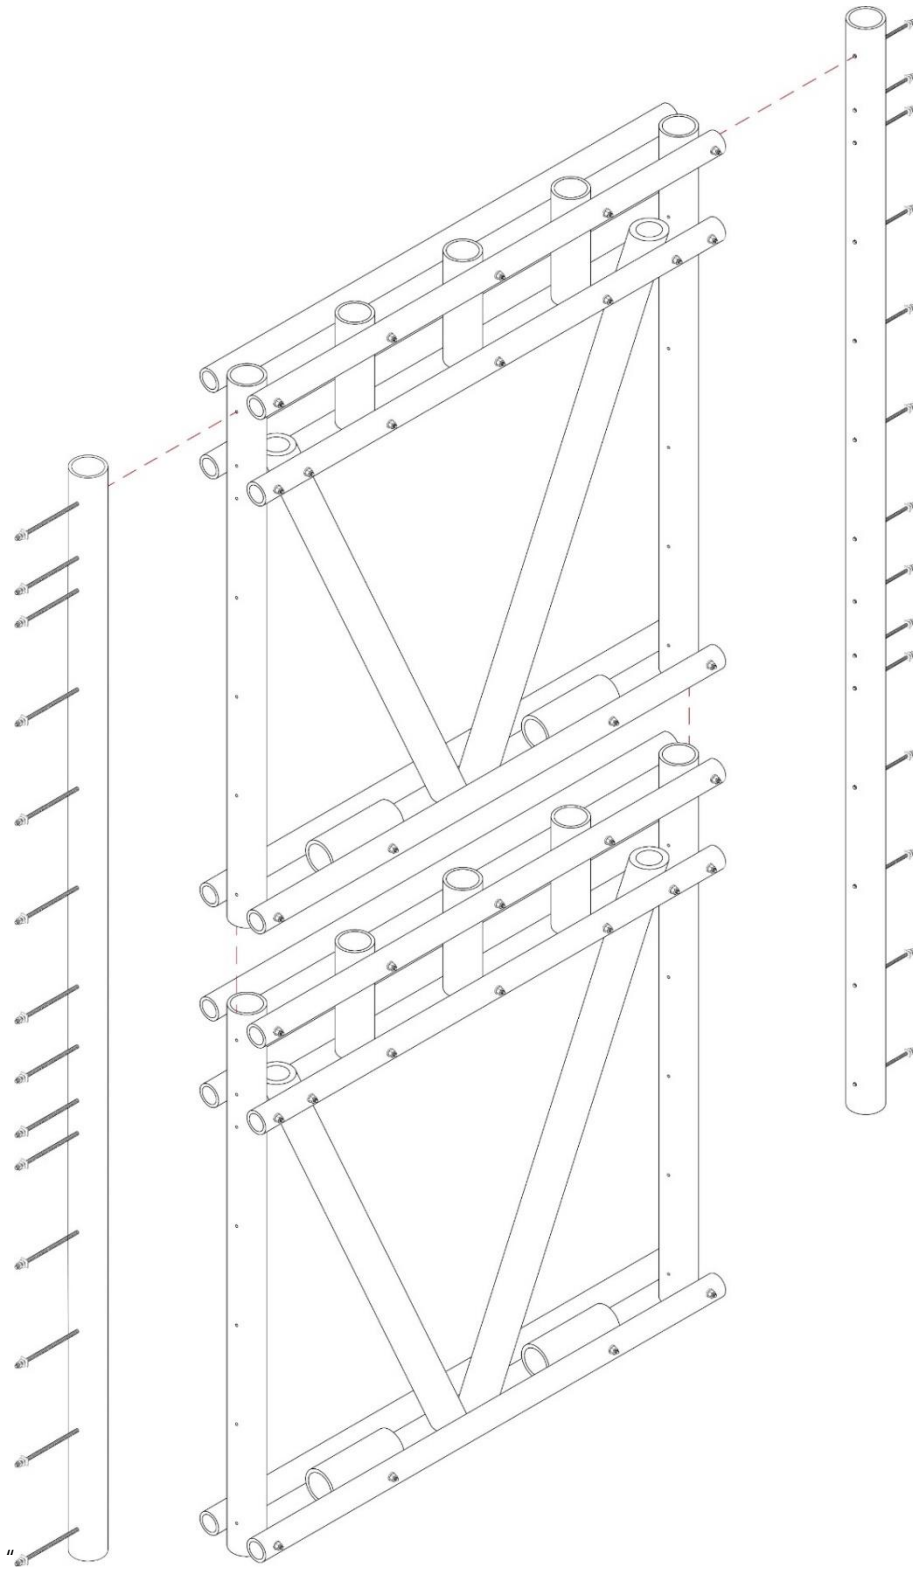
Spaccato assometrico dell'assemblaggio del prototipo con pannello di "tipo B"
